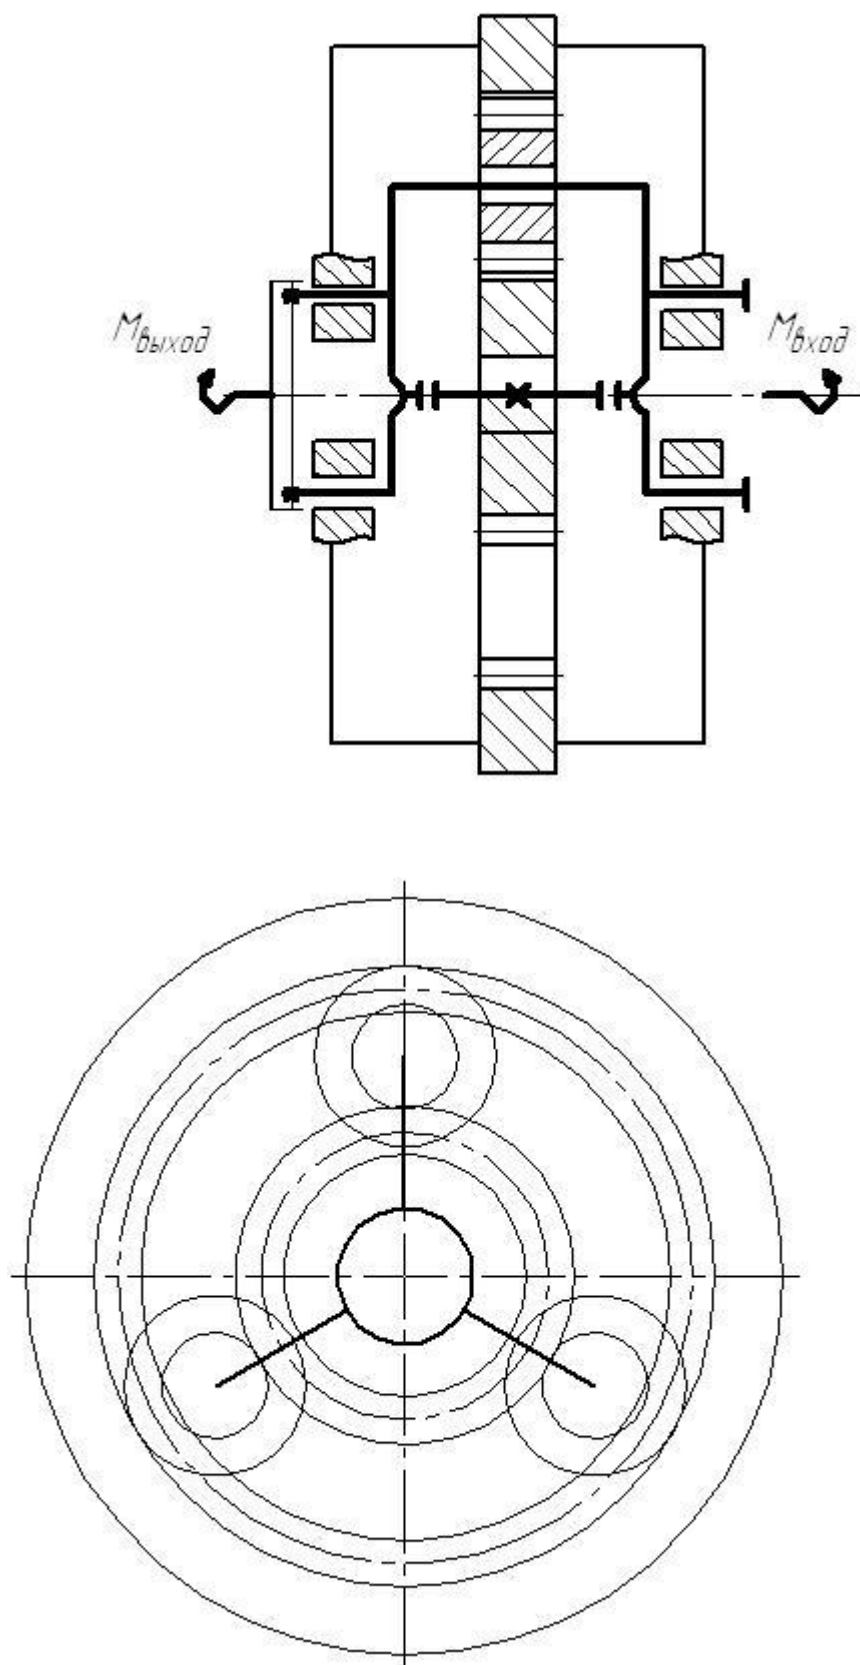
Кинематическая схема узла планетарного редуктора
